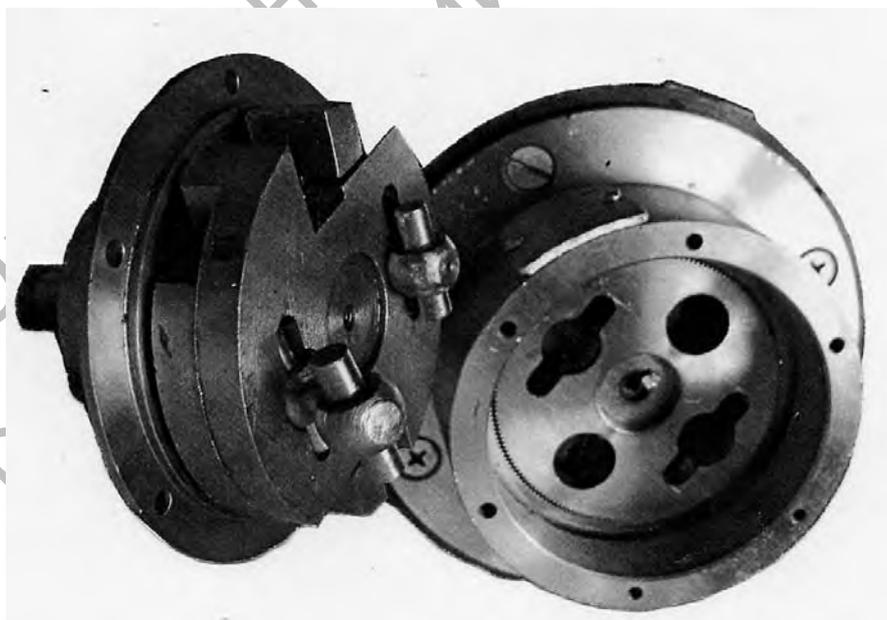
Планетарный механизм с двумя карданами и механизмом выборки люфта
